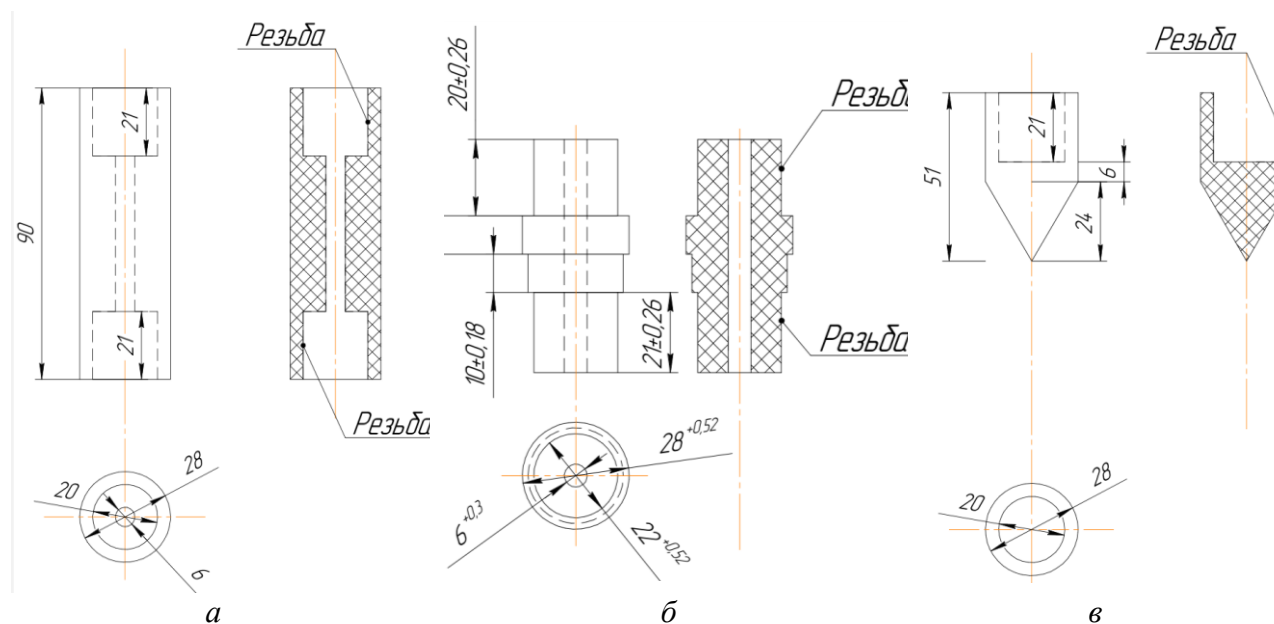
Сборочные элементы измерительной штанги: *а* – втулка с внутренней резьбой; *б* – соединительный элемент посадки колец с внешней резьбой; *в* – наконечник измерительной штанги с внутренней резьбой
